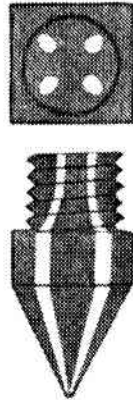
а) Винтовой шипъ съ 4-мя стальными жвалами, б) поперечный разрѣзъ его.
